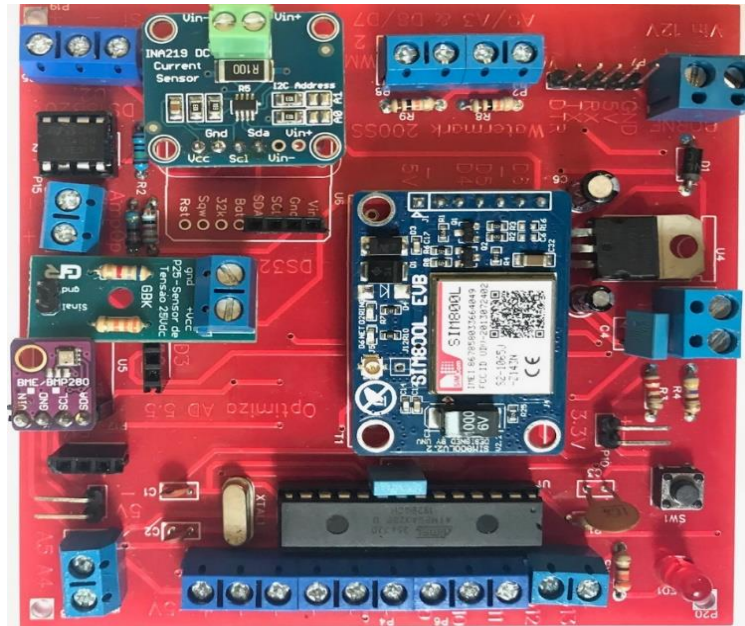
Placa de circuito impresso com os componentes, módulos e sensores.
